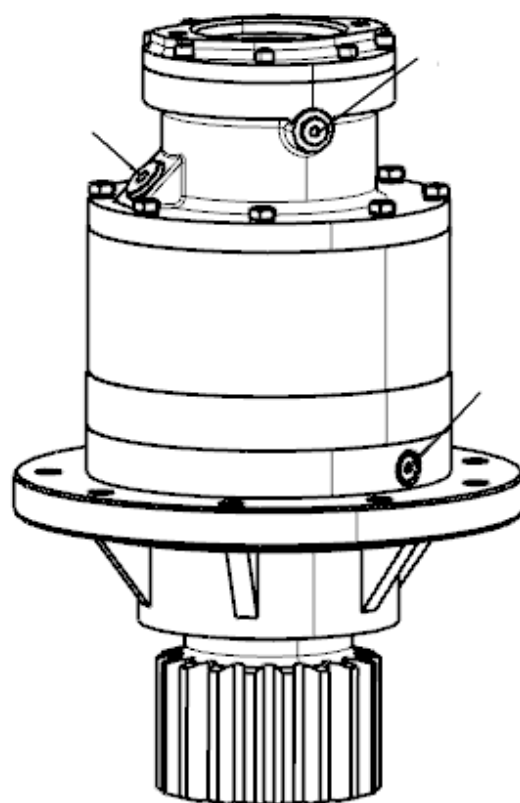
Схема расположения каждой заливной горловины редуктора.
